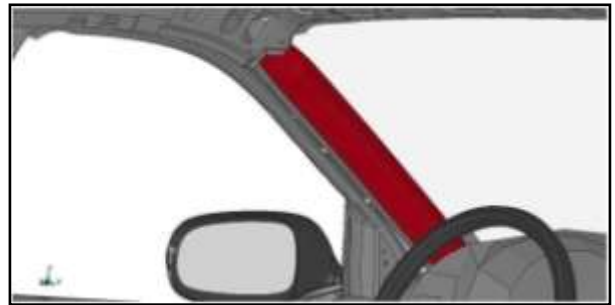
Konstrukce připevněná k platformě vozidla (10)
